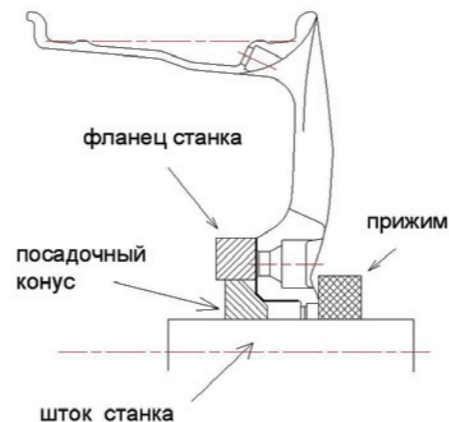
Закрепление колеса по привалочной плоскости и центральному отверстию
